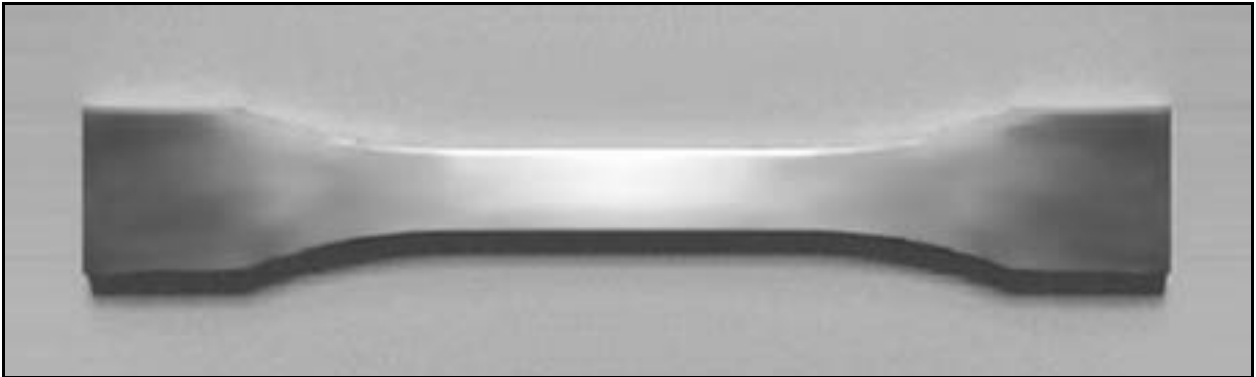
Probeta para determinar el límite de fatiga de la junta soldada.
